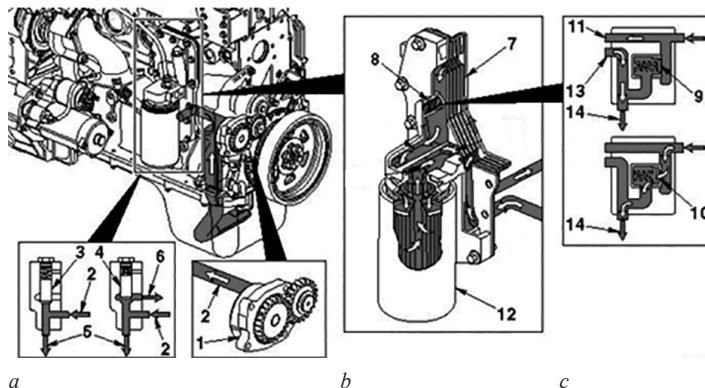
Схема забора масла из поддона картера (а), подключения масляного насоса (b) и потоки масла в крышке маслоохладителя системы смазки двигателя (c)
